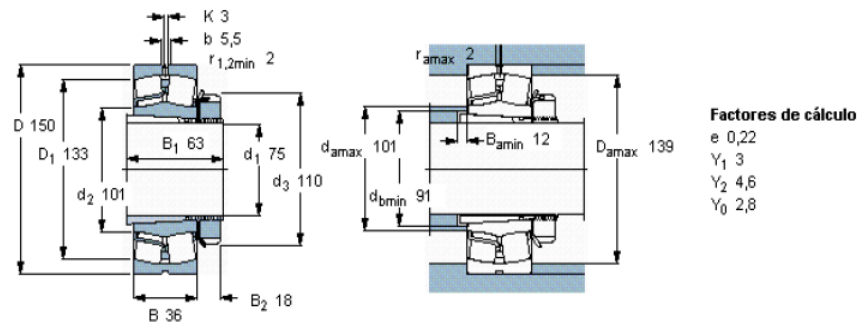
Rodamiento SKF 22217EK+H317 [23].
